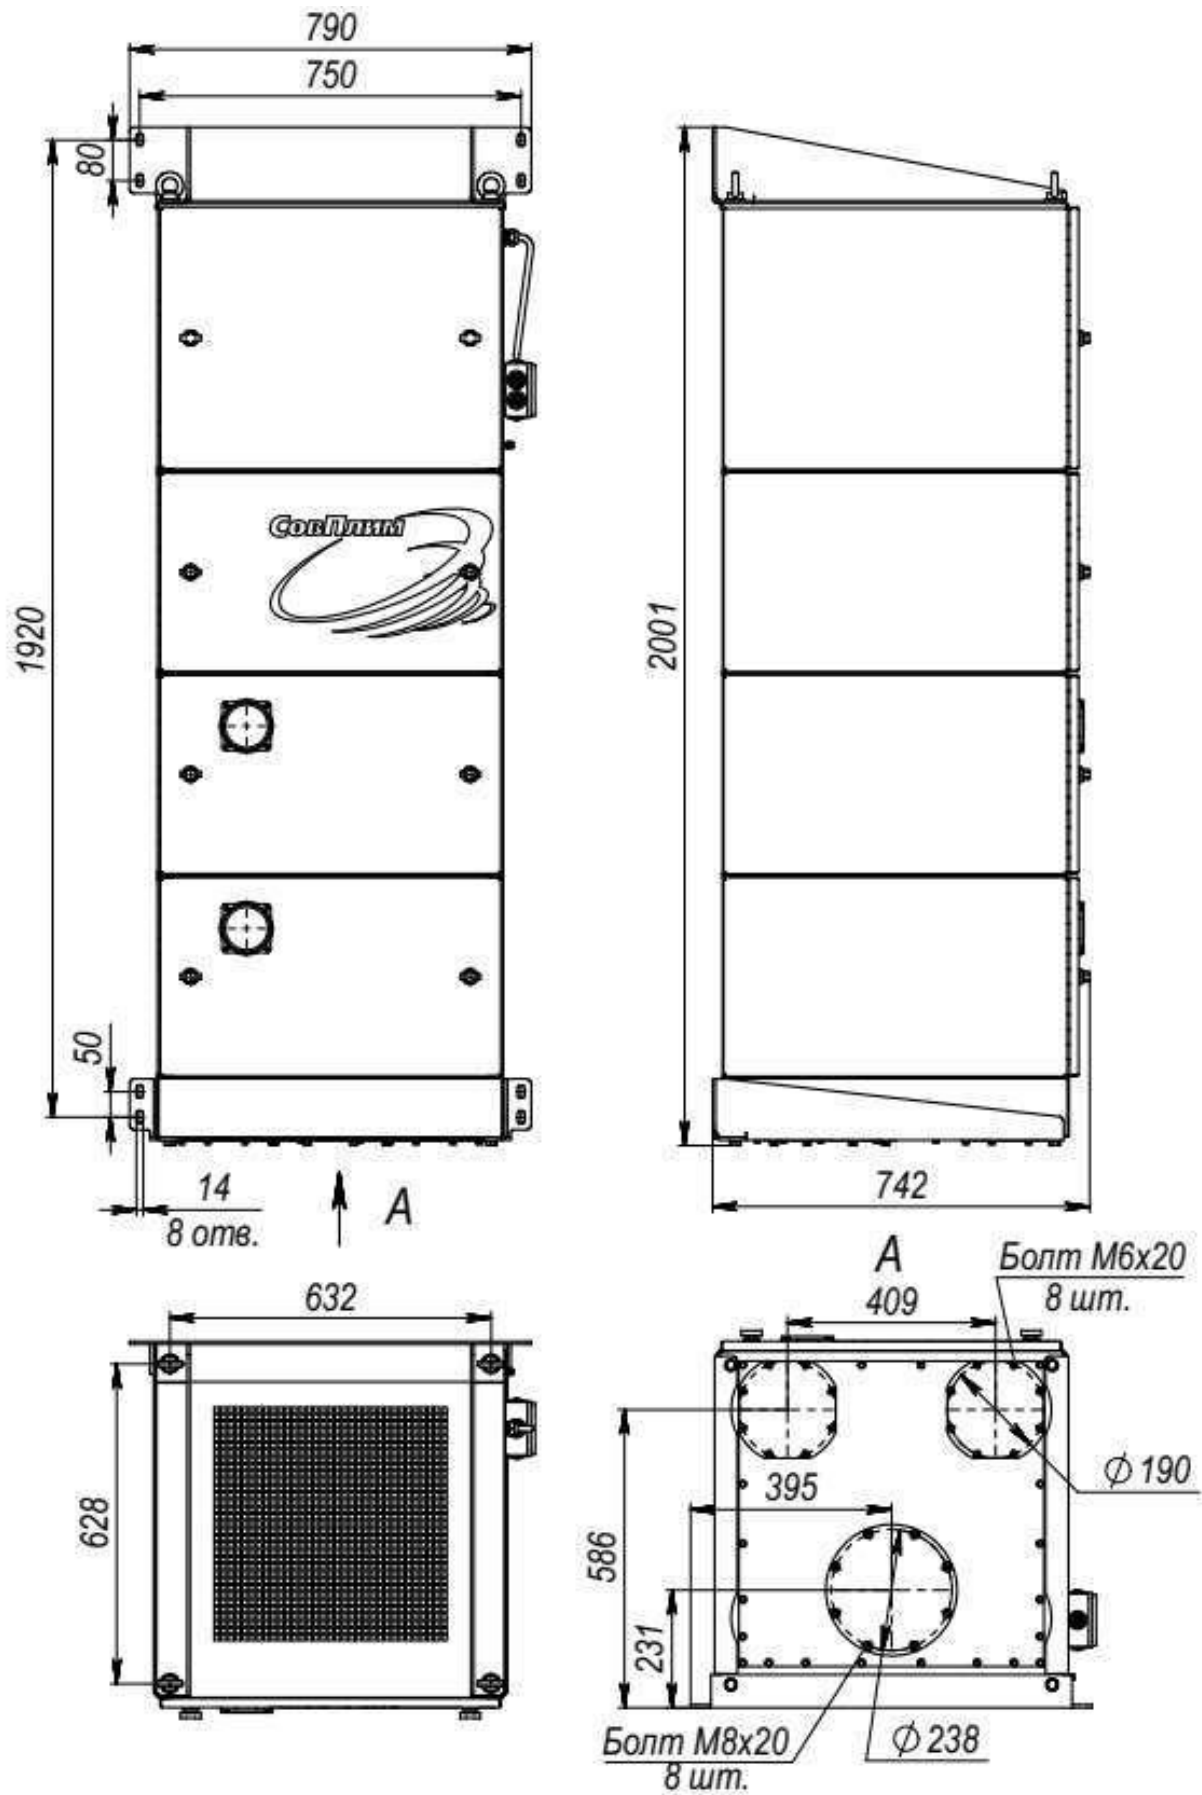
Габаритные размеры фильтра MF-H-42-F6
